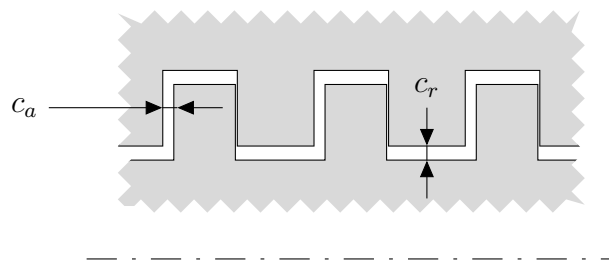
Gewindenspiel bei rechteckigem Gewindeprofil.
